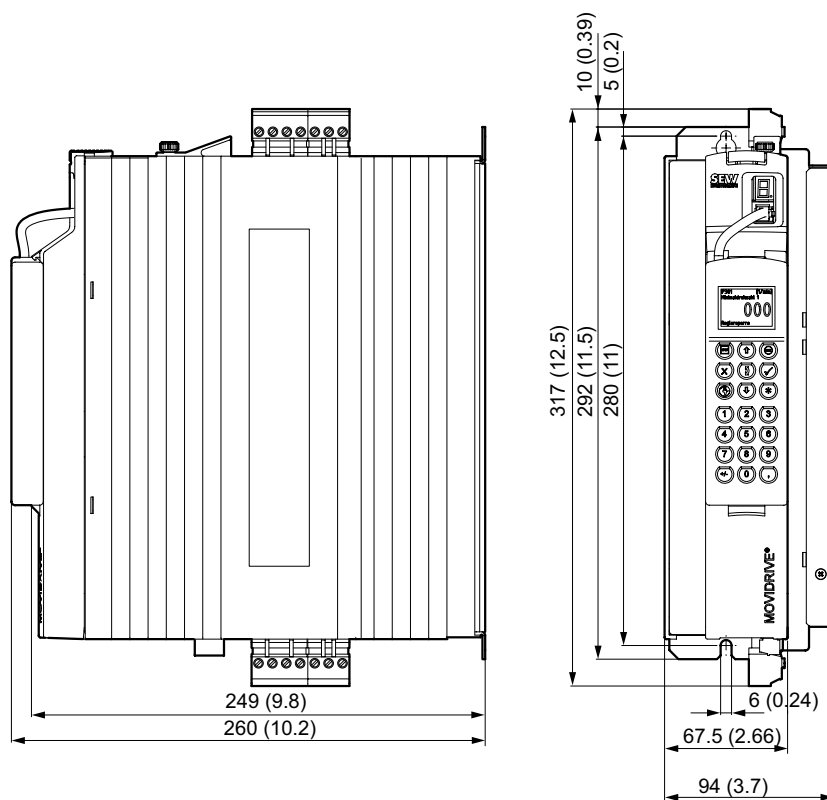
Dimensões MDX60B, tamanho 0M com resistência de frenagem, em mm (in)
